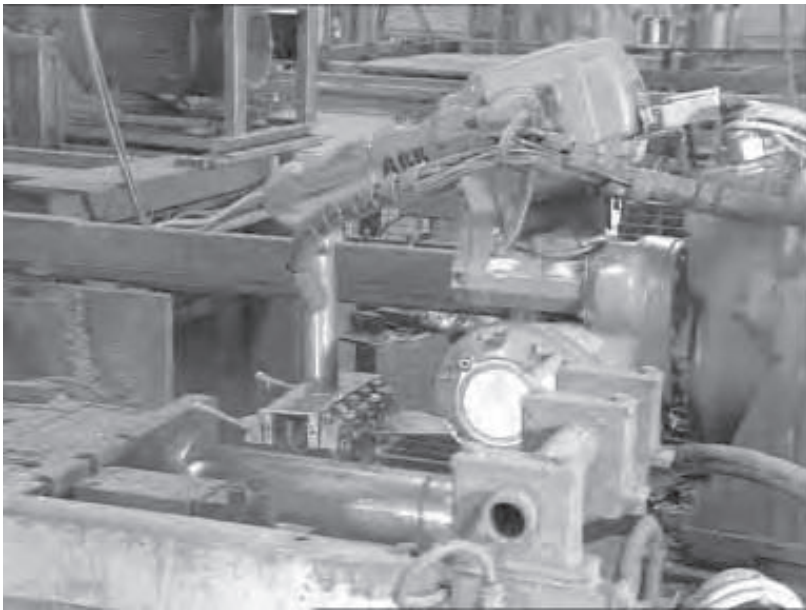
Robot trabajando en molde por inyección. (Cortesía ABB).
